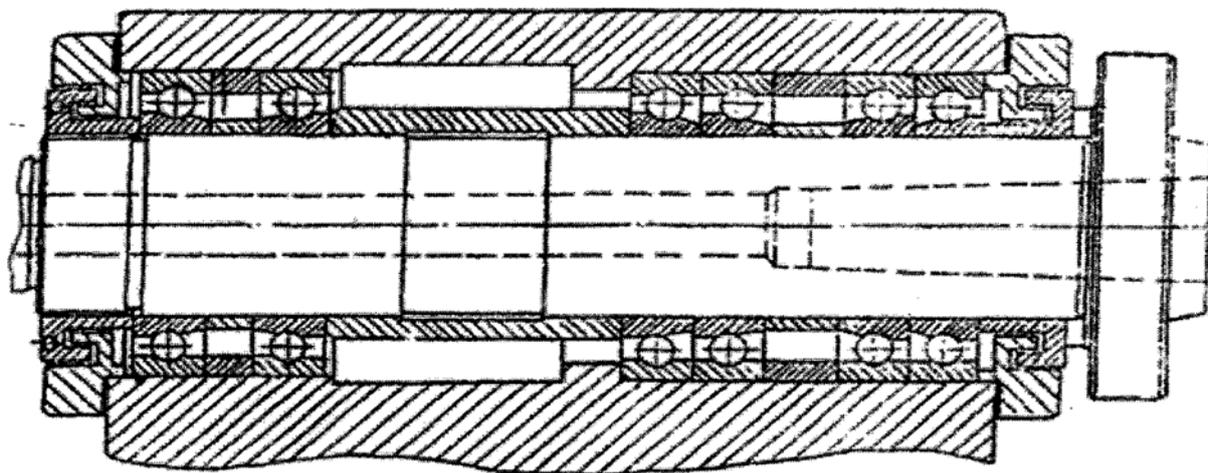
Шпиндельный узел станка с ЧПУ на роликоподшипниках типа 3182100 в обеих опорах и на упорно-радиальном подшипнике типа 178000 в передней опоре
